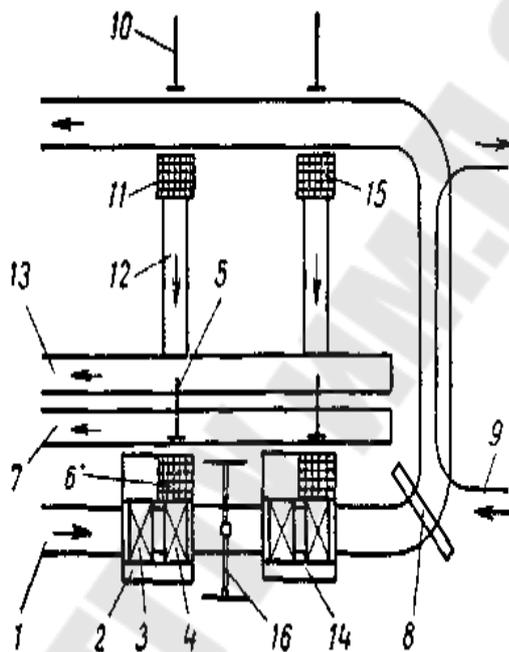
Планировка установки Горьковского автозавода для выбивки форм блоков цилиндра с крестовинами в нижних опоках
